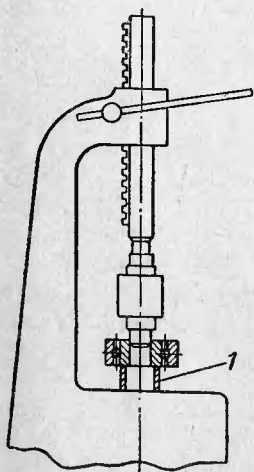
Запрессовка подшипника на вал с помощью ручного прессы и монтажного стакана.
